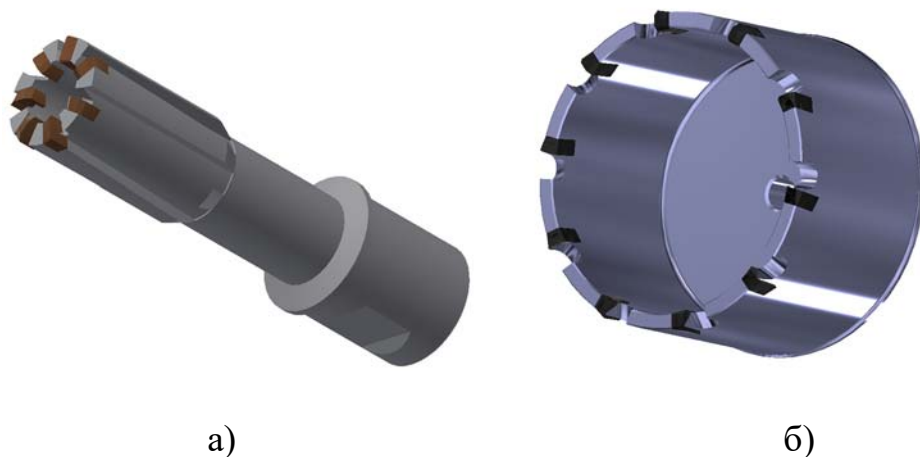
Корончаті свердла зі змінними пластинами
